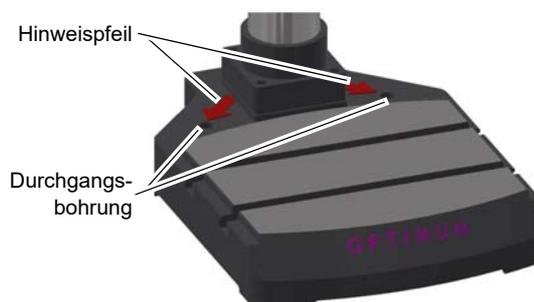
Kennzeichnung der Befestigungspunkte an Tischbohrmaschinen
